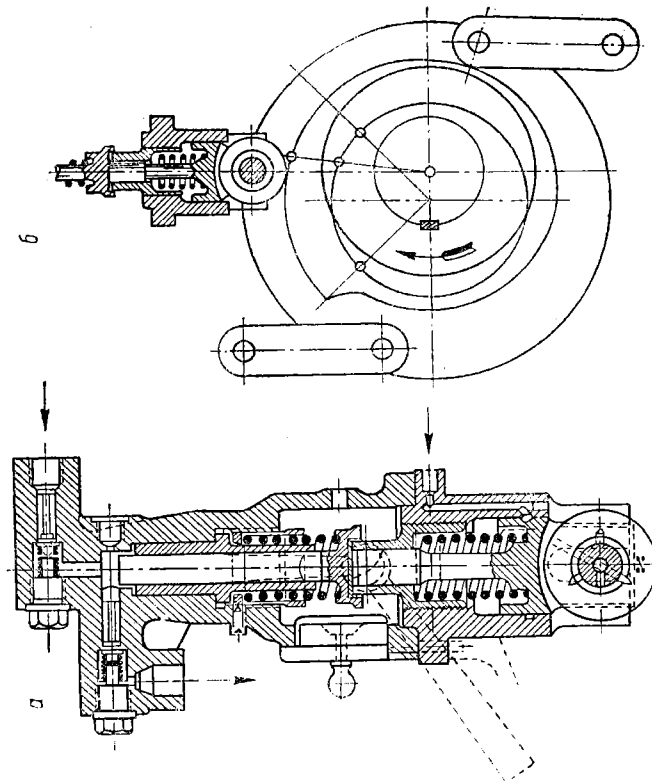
Топливный насос двигателя Ч42,5/60:
